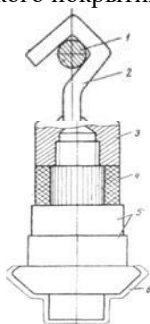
Подвесное приспособление для хромирования шеек под подшипники на ведущей шестерне заднего моста автомобиля I A 5-
